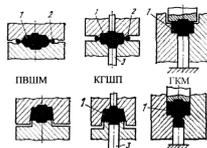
Схемы штамповки на различных видах оборудования: 1 – ручей штампа; 2 – облой; 3 – выталкиватель
